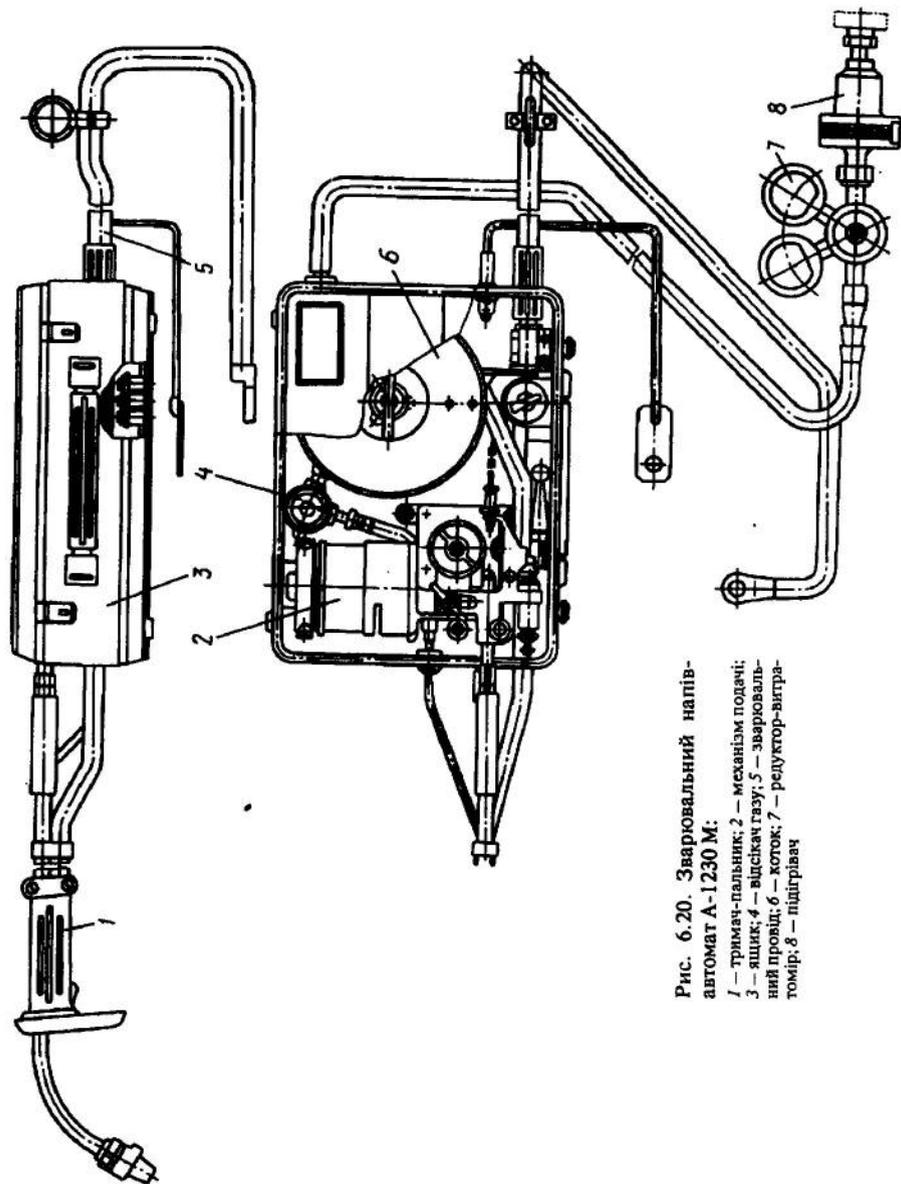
Зварювальний напівавтомат А-1230 М:
